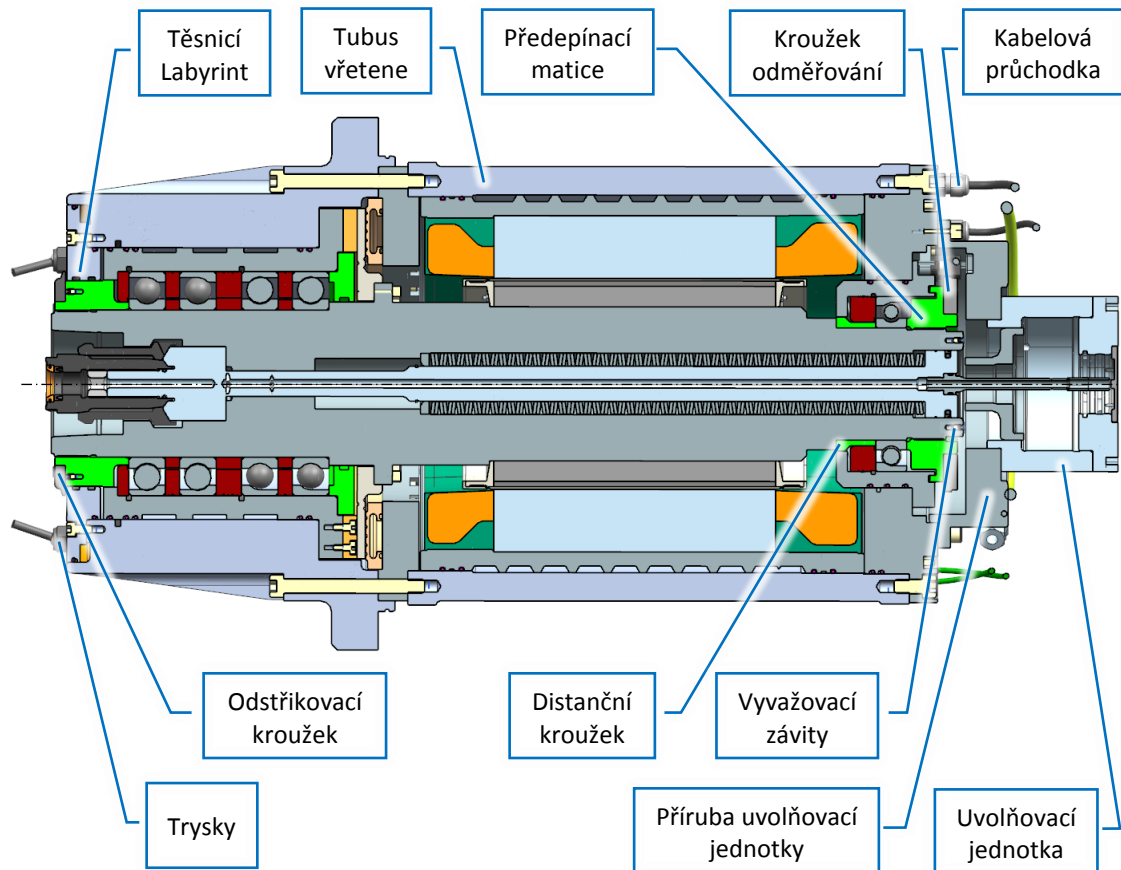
Řez konstrukčním uzlem tubusu vřetene
